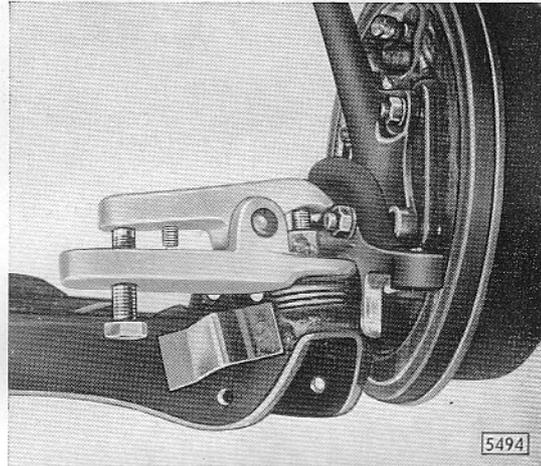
Kugelbolzen des Traggelenkes mit Kugelbolzen-Ausdrückvorrichtung S-1235 aus Achsschenkel herausdrücken
